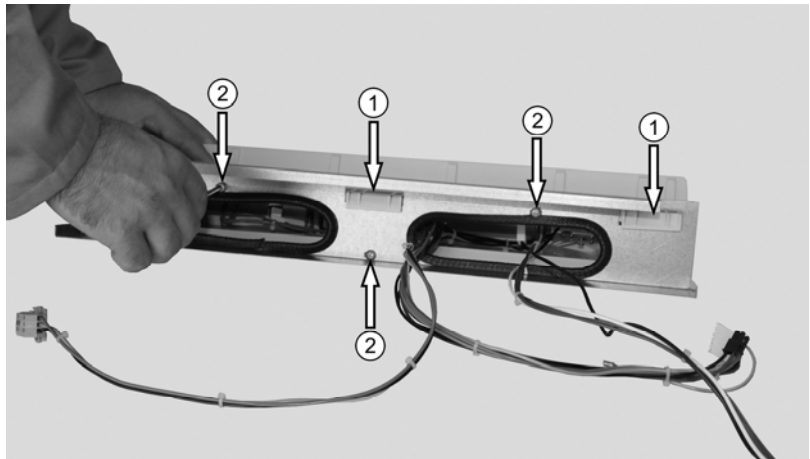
Das Schaltfeld mit den drei Haken ① in das Halteblech einstecken und anschließend mit drei Schrauben ② befestigen.
